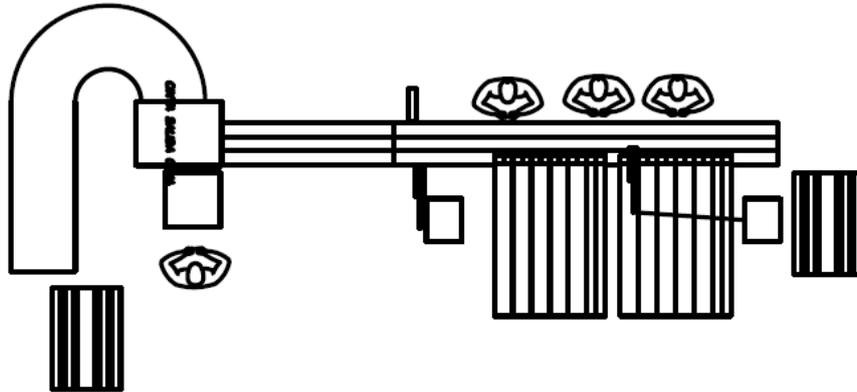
Layout actual montaje biberón. Fuente: Elaboración propia.
